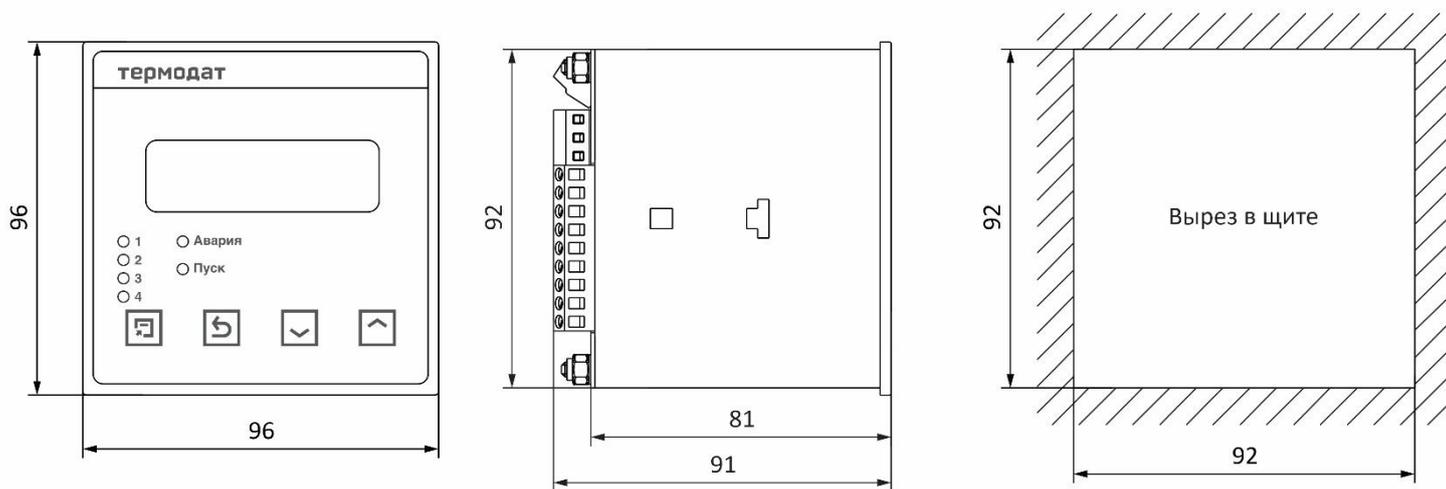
Габаритные размеры прибора Термодат-14Е5-А...
